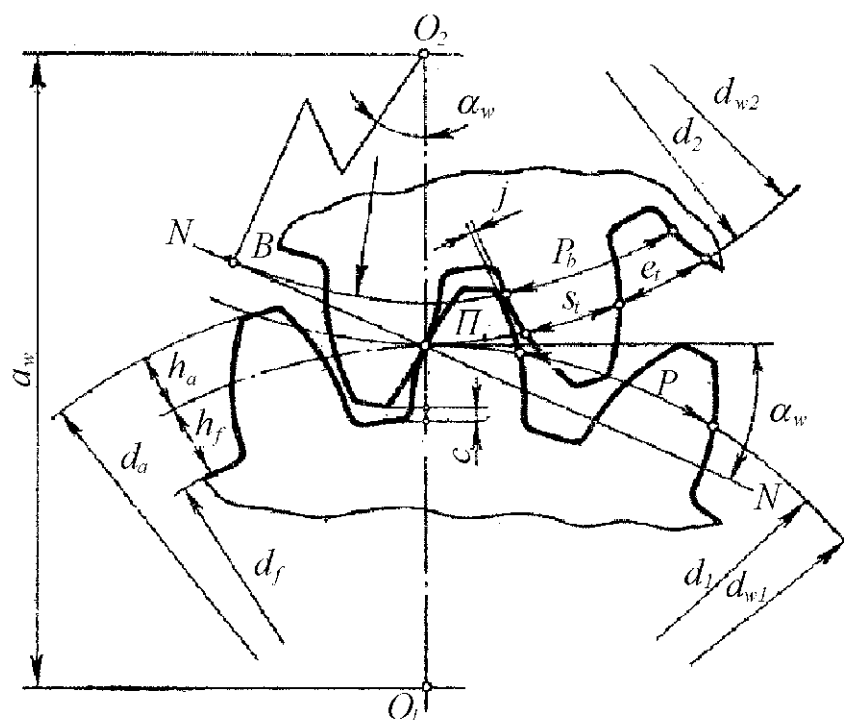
Эвольвентная цилиндрическая передача
